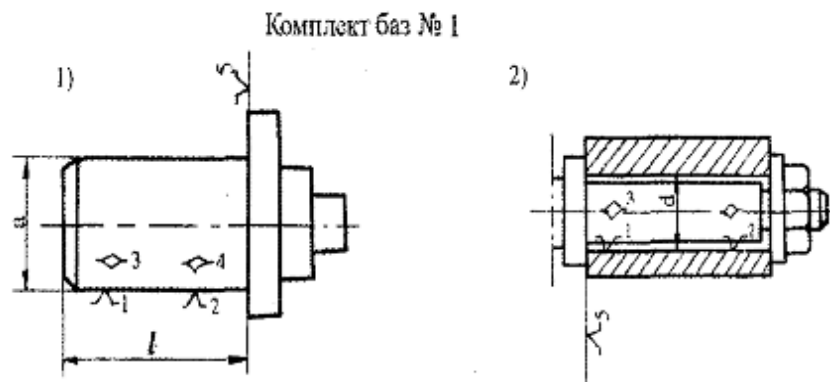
Теоретичні схеми базування довгих заготовок типу тіл обертання
